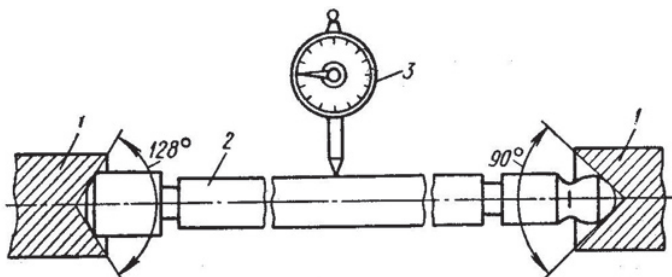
Толкающая штанга, проверяемая на погнутость: 1 — призмы приспособления; 2 — толкающая штанга; 3 — индикатор
